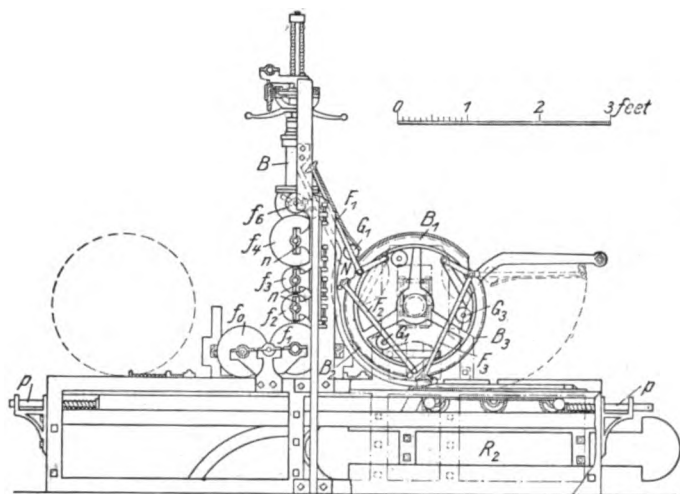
Erste Zylinderdruckmaschine (1812), Vorderansicht
